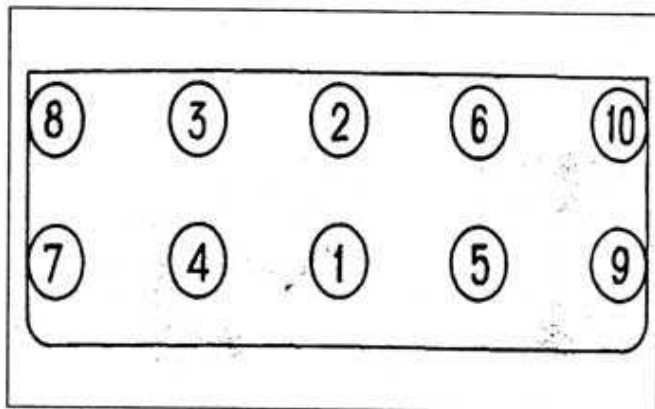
Последовательность затяжки гаек крепления головки цилиндров
